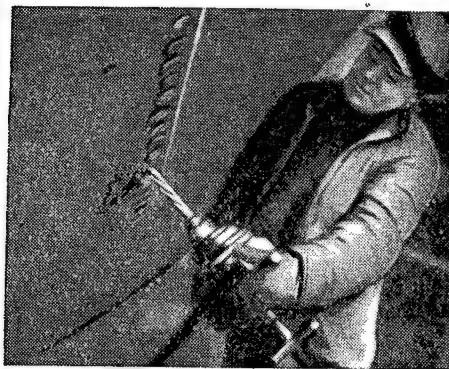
Сверление отверстий пневматической сверлильной машинкой
